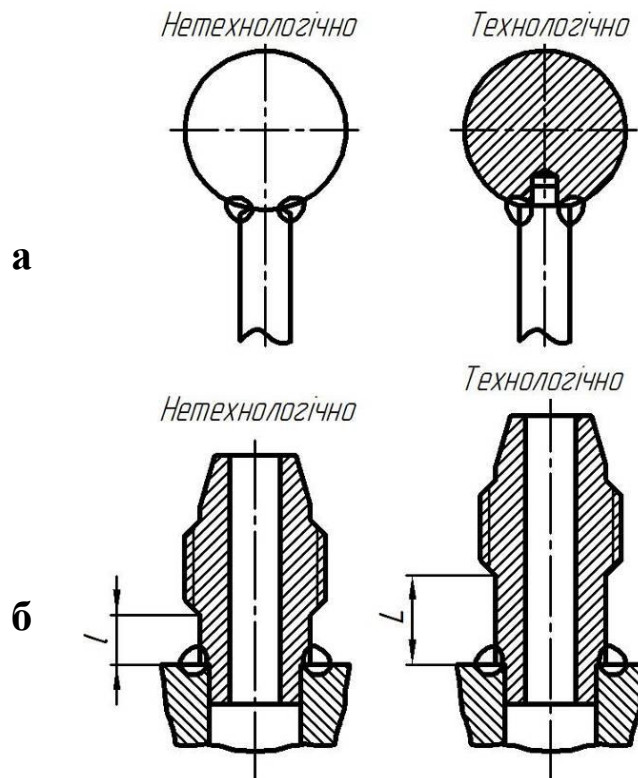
Фіксація положення вихідних заготовок перед зварювання:
